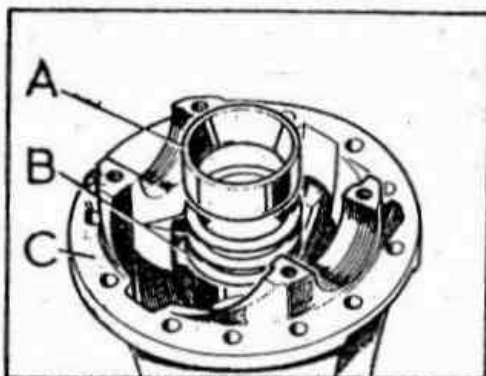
Pista exterior del cojinete de extremo del piñón
